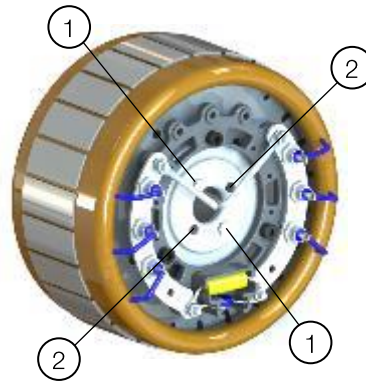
Befestigung und Bohrungen zum Herausziehen des Erregerrotors
